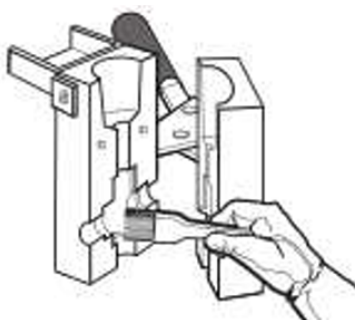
Eliminar los restos de la cámara de soldadura por medio de la brocha
